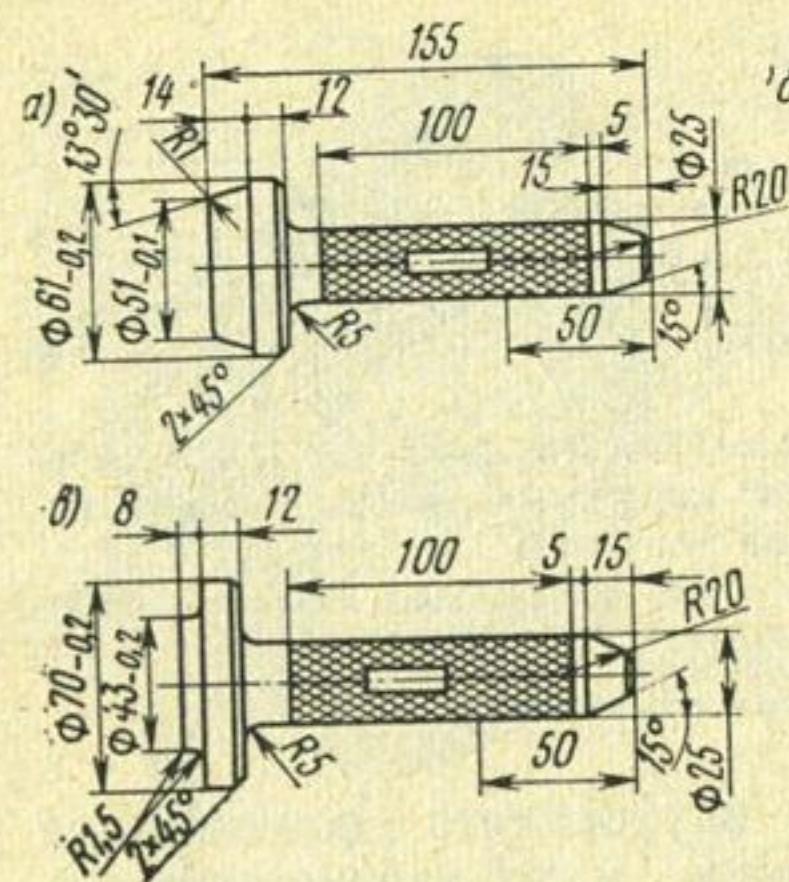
Оправки для запрессовки наружных колец подшипников ступицы и ее сальника:
